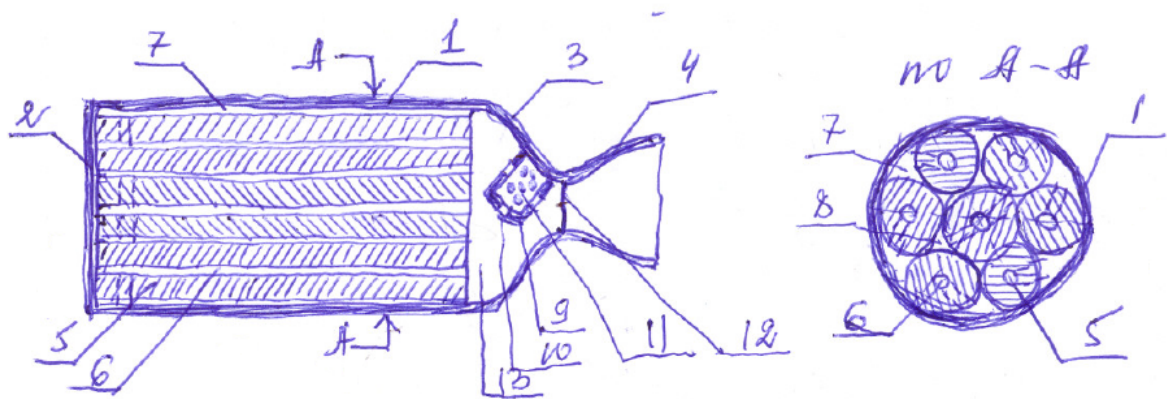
Обозначение: 1 — обечайка корпуса двигателя, 2 — переднее днище двигателя, 3 — сопловое днище двигателя, переходящее в сопло, 4 — расширяющаяся часть сопла (конфузор), 5 — шашка твёрдотопливного заряда, 6 — канал шашки, 7 — зазор между наружной поверхностью шашки и внутренней поверхностью корпуса двигателя, 8 — зазор между шашками, 9 — корпус воспламенителя, 10 — отверстие в корпусе воспламенителя, 11 — заряд дымного ружейного пороха (ДРП), 12 — заглушка, 13 — предсопловой объём.
